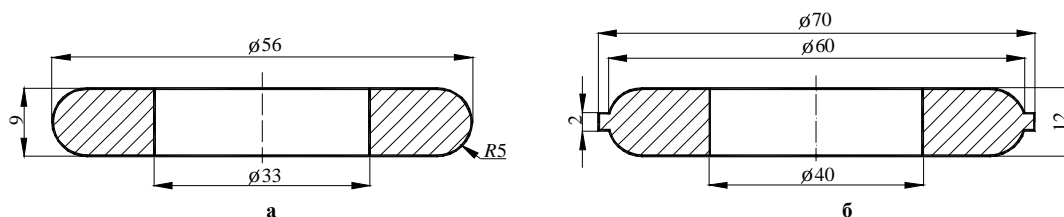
Ролик (а) і заготовка ролика до спікання (б)
